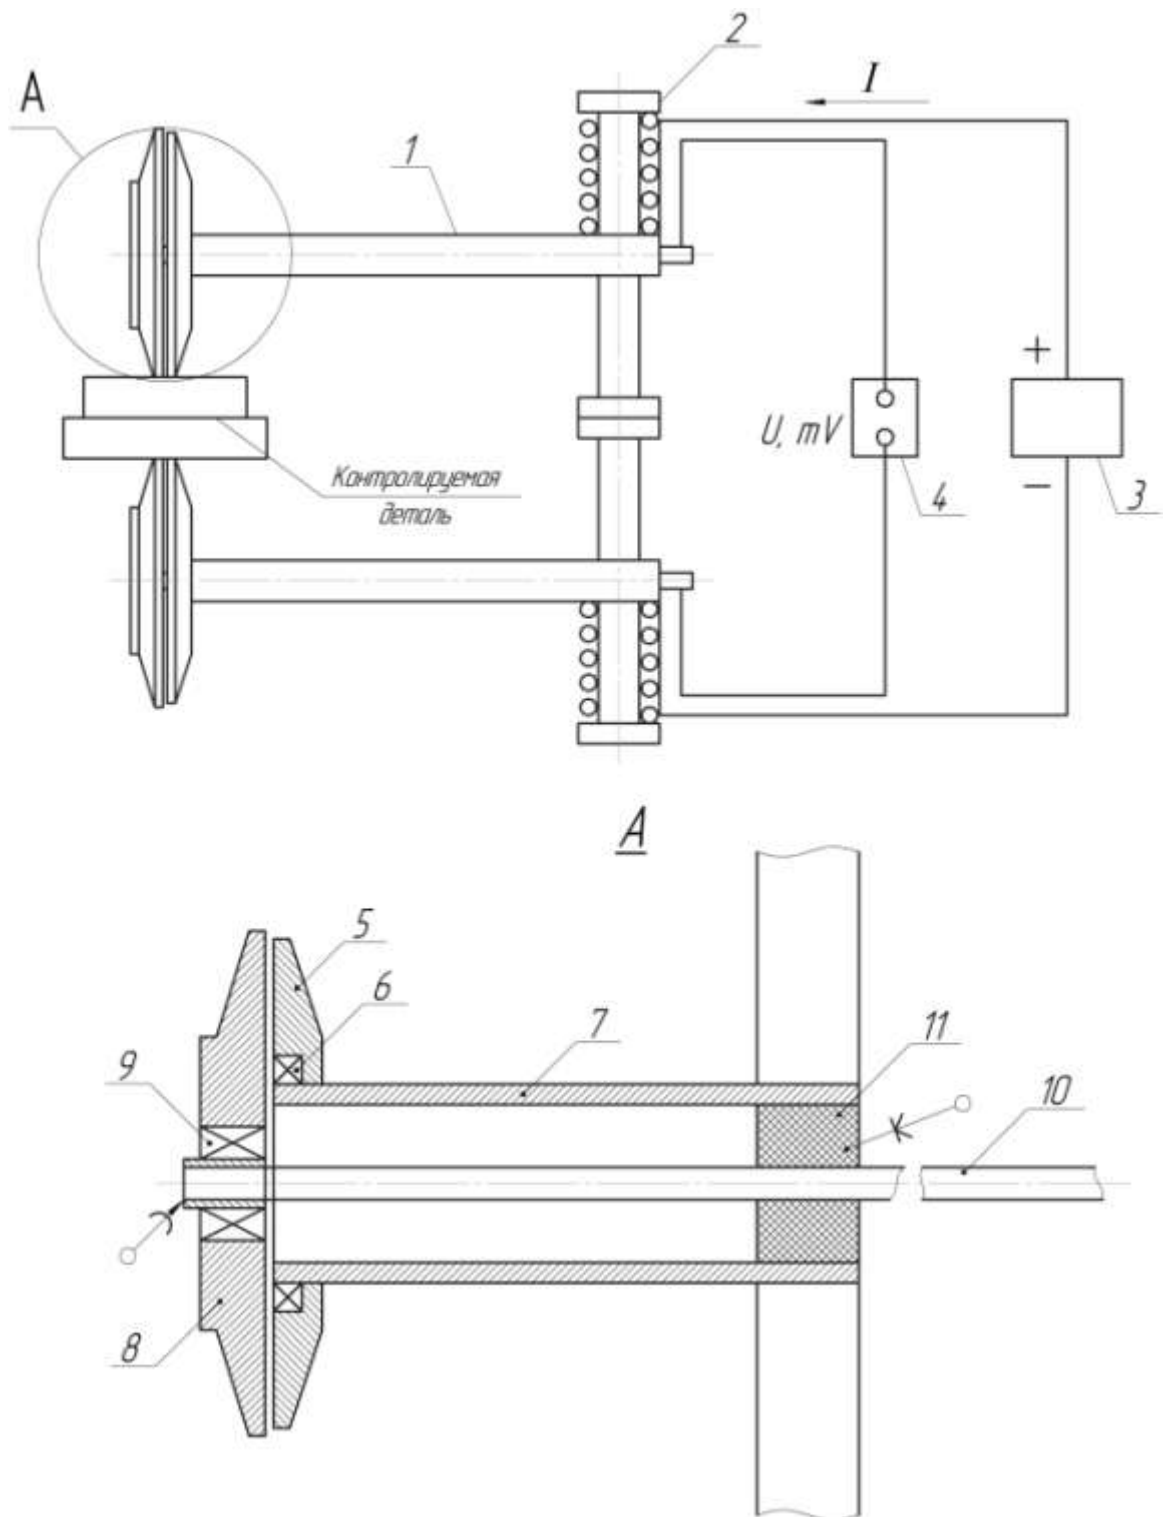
Схема устройства для контроля измерением электросопротивления: 1 – электроды; 2 – корпус; 3 – источник питания; 4 – прибор измерительный; 5 – токовый ролик; 6,9 - подшипники; 7 - ось трубчатая; 8 – потенциальный ролик; 10 – упругая ось; 11 – изолирующая втулка
